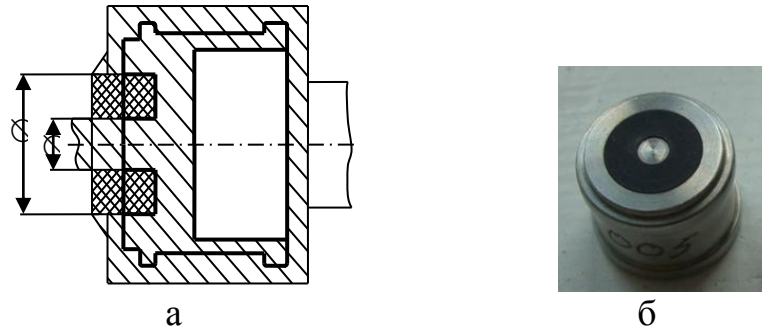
Заготовка для виготовлення золотника із кільцевою гумовою вставкою (а) та зовнішній вигляд золотника після полірування торця (б)
